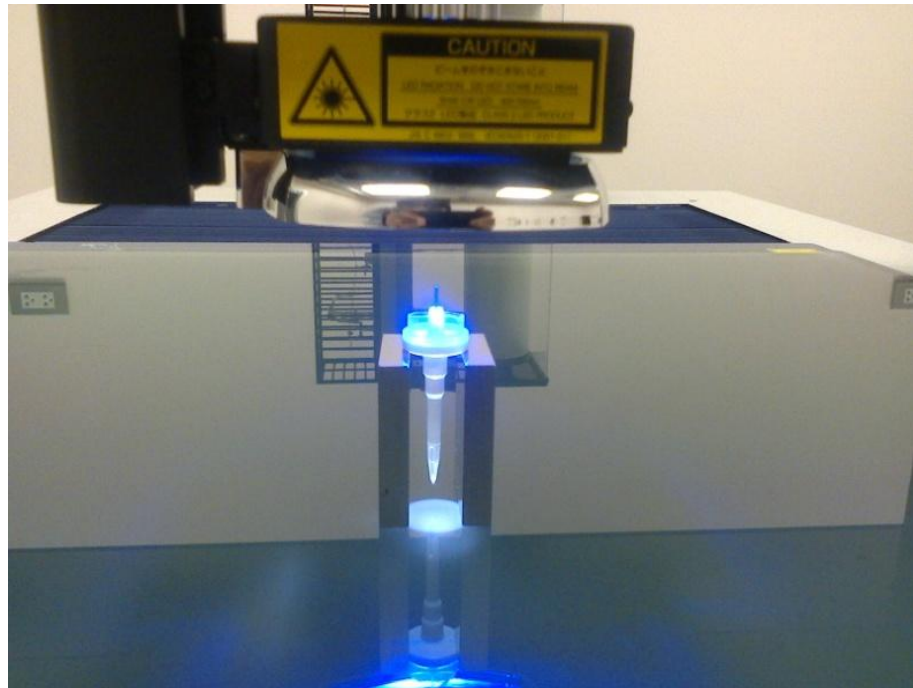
การแสดงผลของเครื่อง CNC Vision Measuring Machine สำหรับ IV Set 20 no.2
